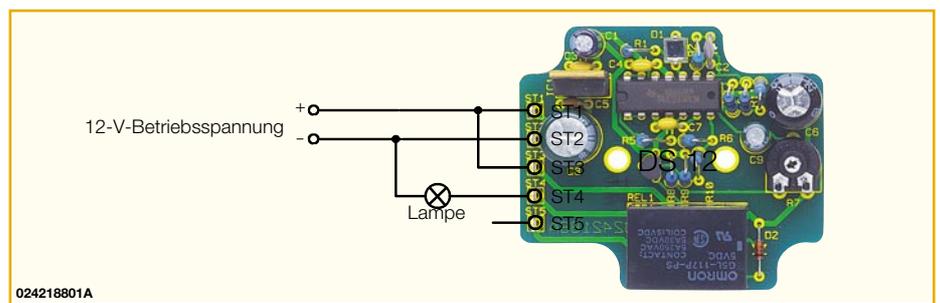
Beispielkonfiguration mit dem Dämmerungsschalter
